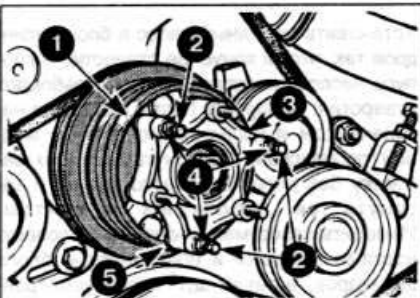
Регулировка зазора электромагнитной муфты вентилятора: 1,3,5 — точки замера зазора; 2 — регулировочные болты; 4 — контргайки
